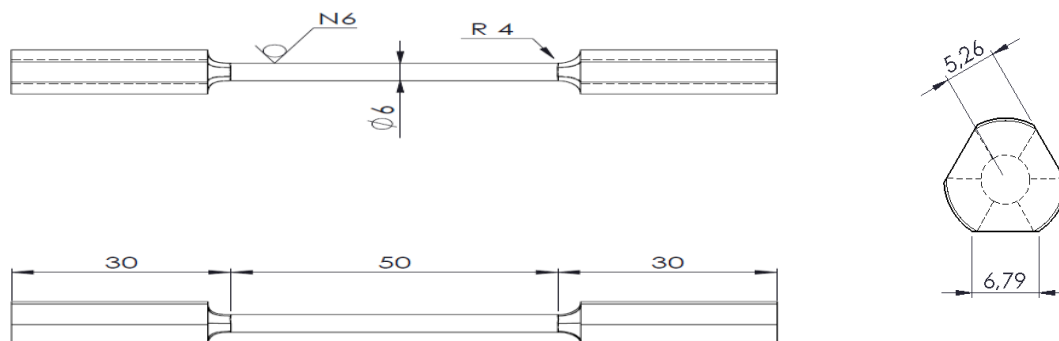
Dimensiones de la probeta según norma ASTM E143-02
